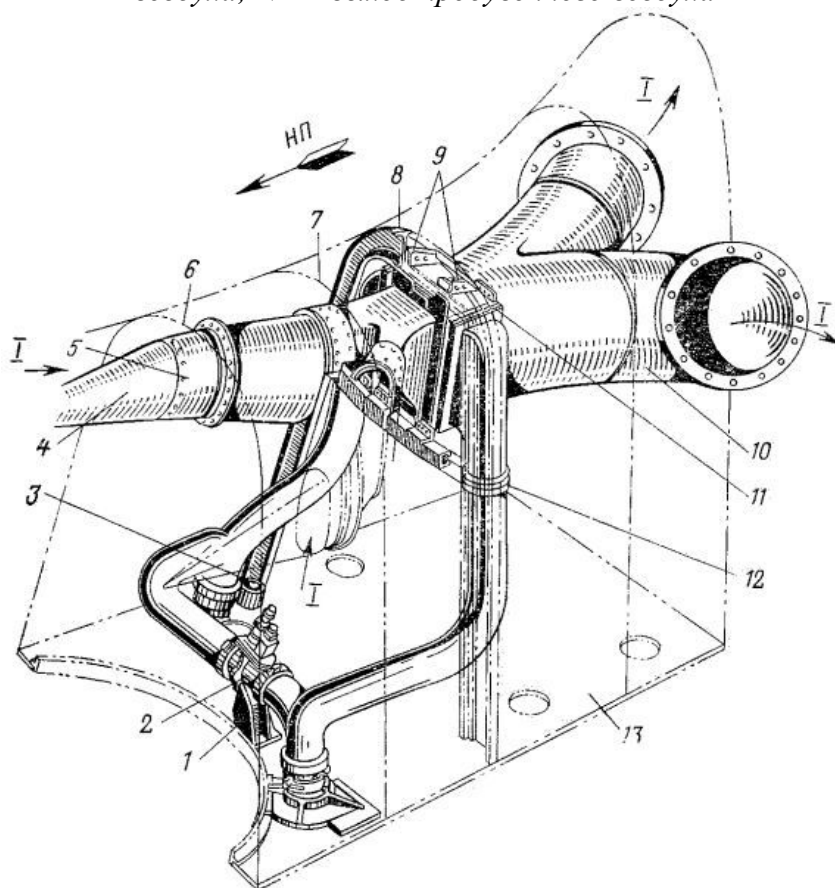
Установка первичного воздухо-воздушного радиатора 4487Т:
